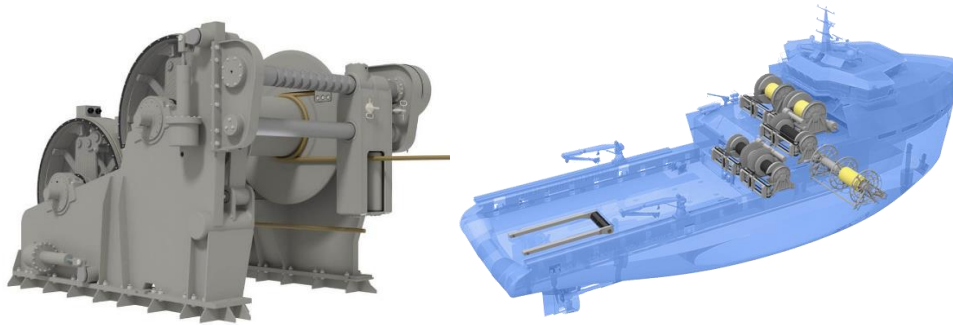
AHTS winch, da fabricante DAMEN e situación a bordo (Damen Unveils Beastly 200T Bollard Pull Anchor Handler, no date)
